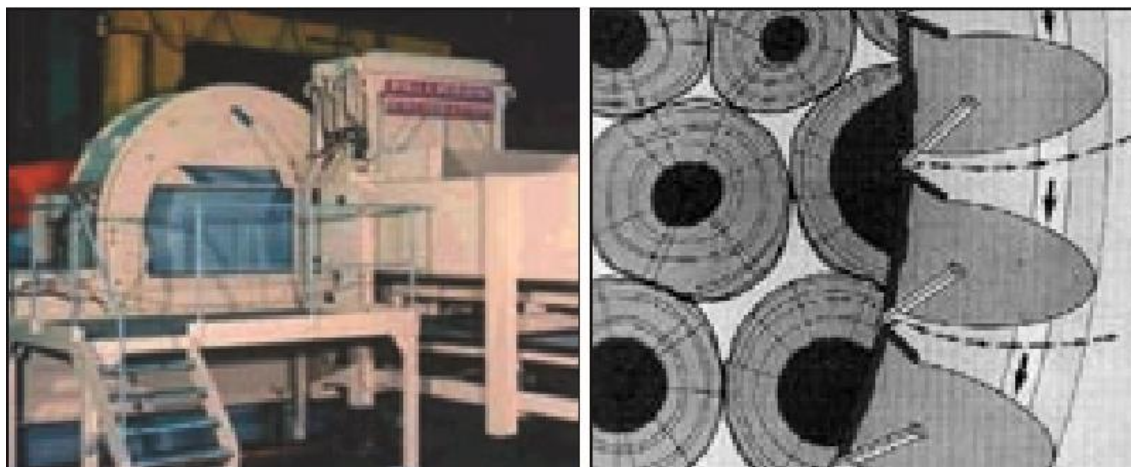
Барабанный станок для получения крупноразмерной стружки
